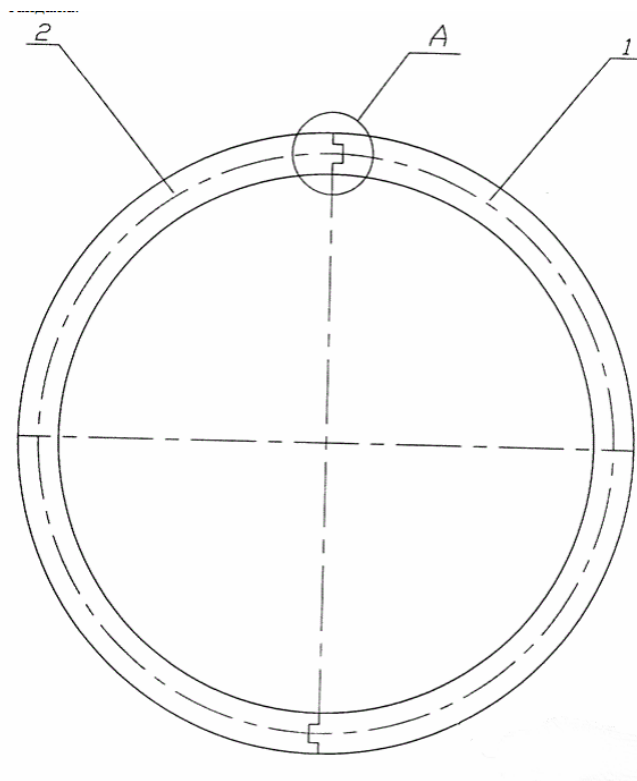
Конструкція бандажа, загальний вигляд
